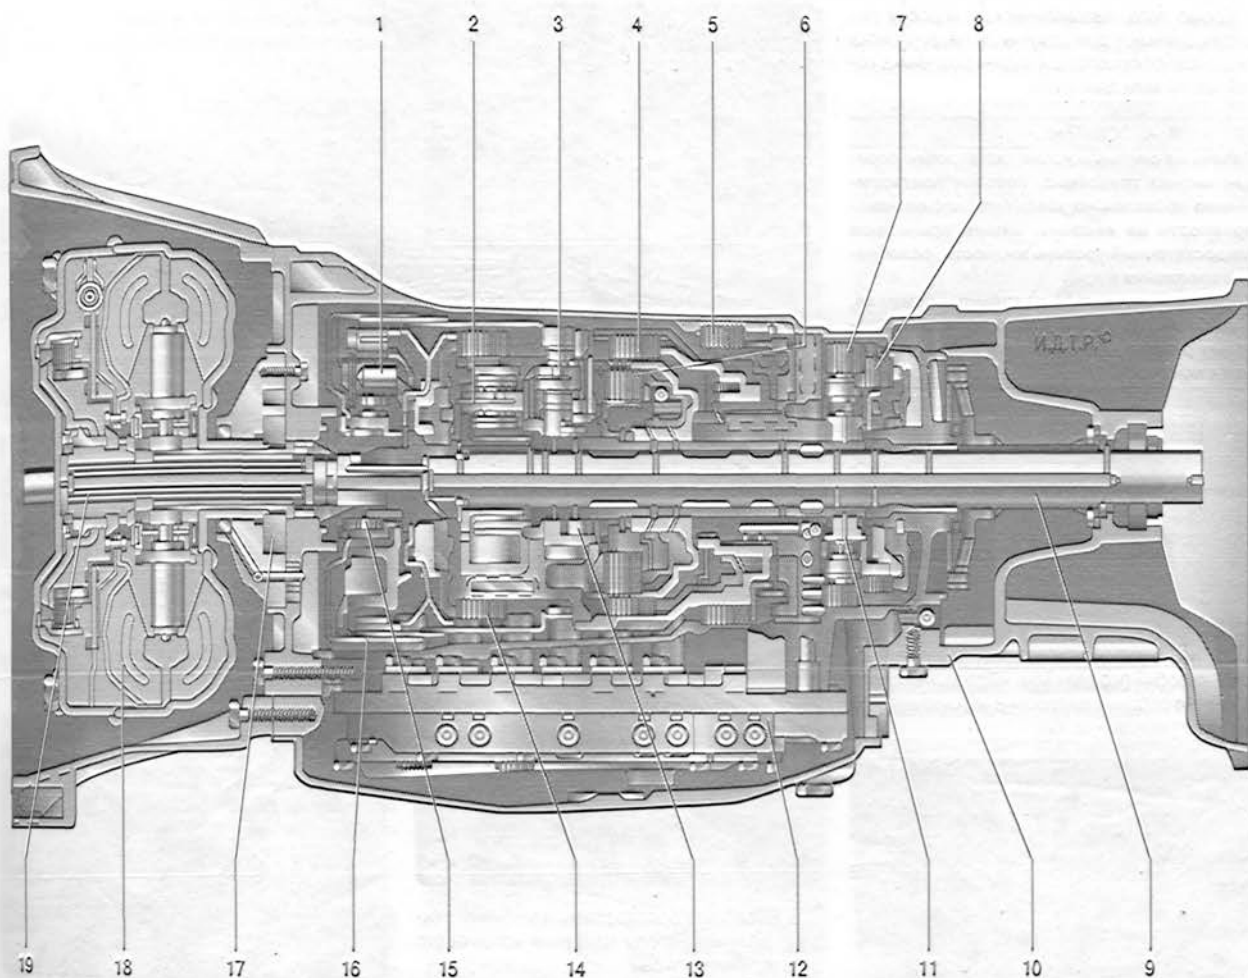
Детали автоматической коробки передач: 1 – планетарный ряд III передачи; 2 – планетарный ряд II передачи; 3 – планетарный ряд I передачи; 4 – муфта прямой передачи; 5 – тормоз задней передачи; 6 – муфта понижающей и задней передач; 7 – тормоз переднего хода; 8 – ленточный тормоз; 9 – выходной вал; 10 – картер; 11 – муфта свободного хода переднего хода; 12 – блок клапанов; 13 – муфта свободного хода I передачи; 14 – муфта свободного хода II передачи; 15 – муфта свободного хода III передачи; 16 – ленточный тормоз; 17 – масляный насос; 18 – гидротрансформатор; 19 – входной вал
